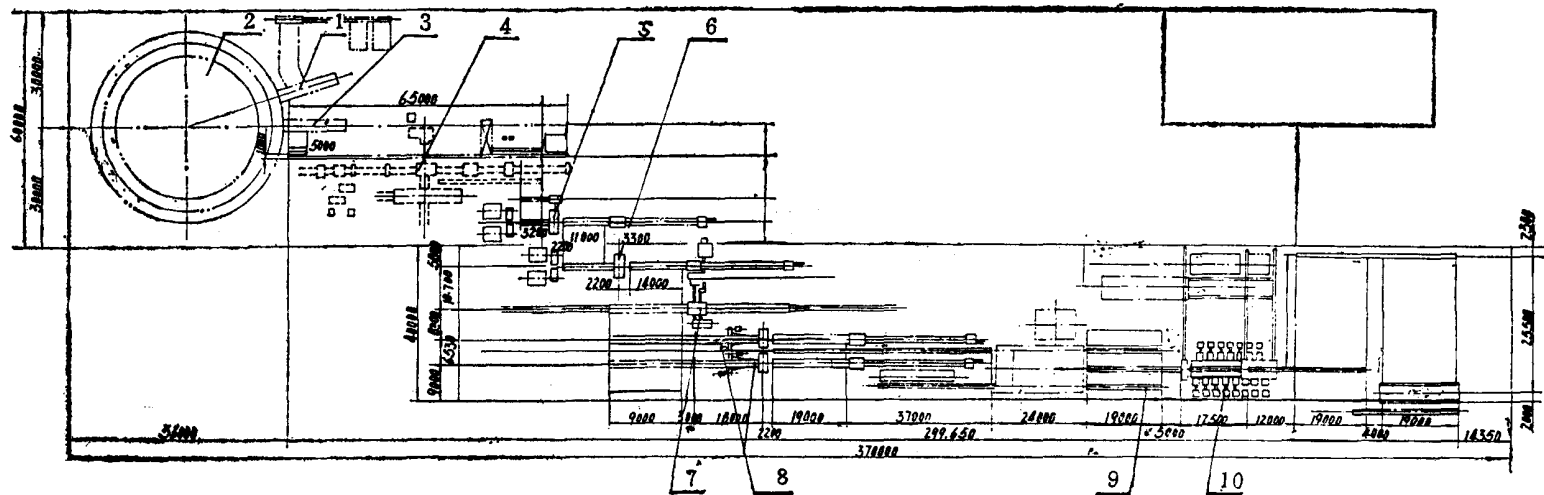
日本川崎制铁公司知多厂 16" 自动轧管机组平面布置图
